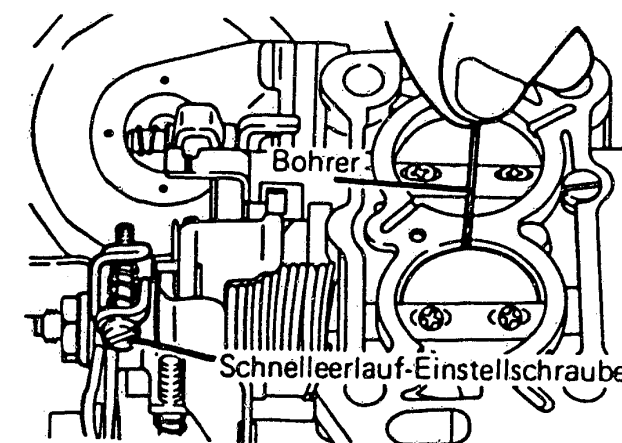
Einstellung des Schnelleerlaufs bei 23°C mit einem Bohrer von 0,51 mm Durchmesser.
